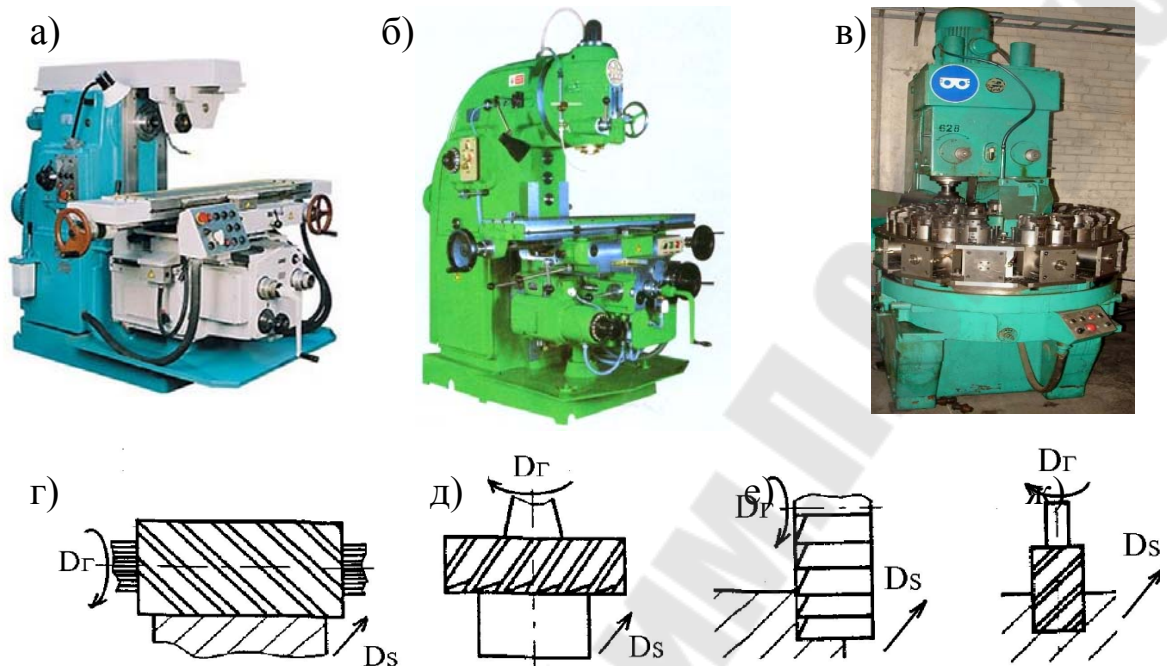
Общие виды фрезерных станков (а - в) и схемы фрезерования плоскости (г - ж)
